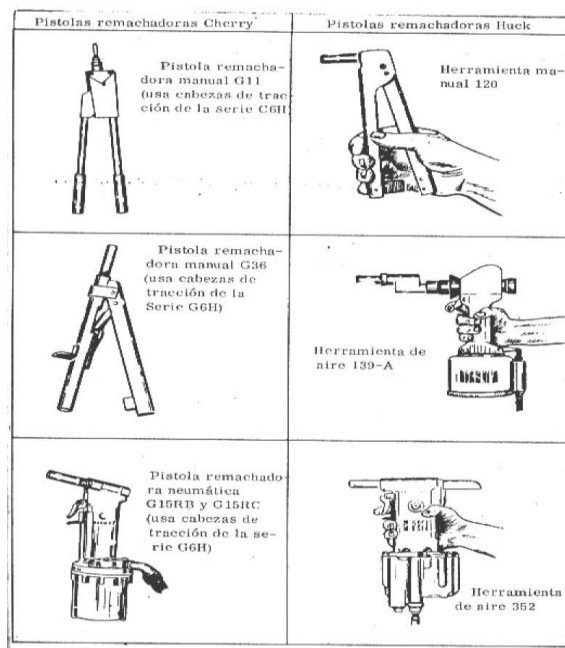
Pistolas Remachadoras de Acción Automática (Cierre por Fricción)
